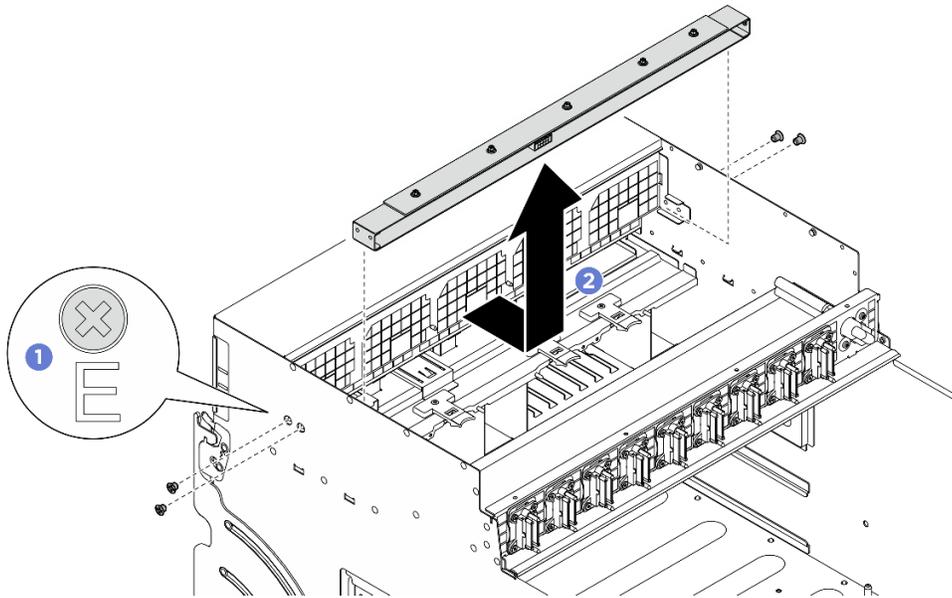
Extracción del conjunto de la placa de control del ventilador frontal
